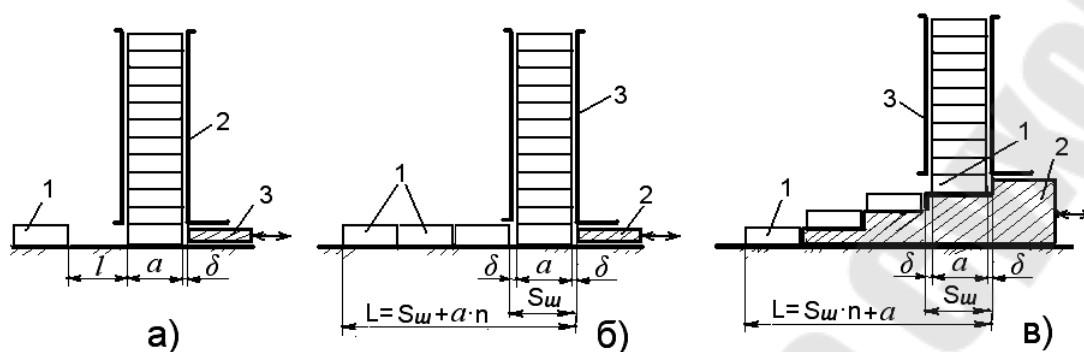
Способы подачи заготовок шибером: 1- заготовка, 2-магазин, 3- шибер
